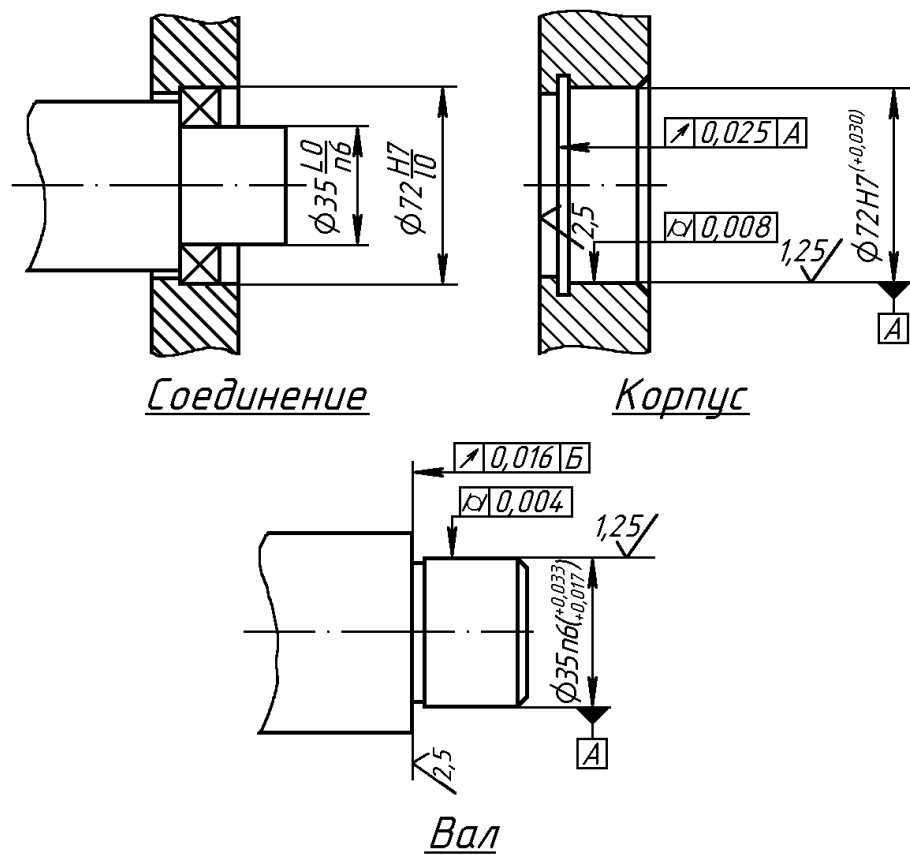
Чертежи подшипникового соединения и его деталей
